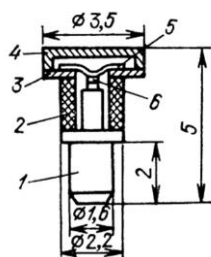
Конструкція корпусного *pin*-діода
